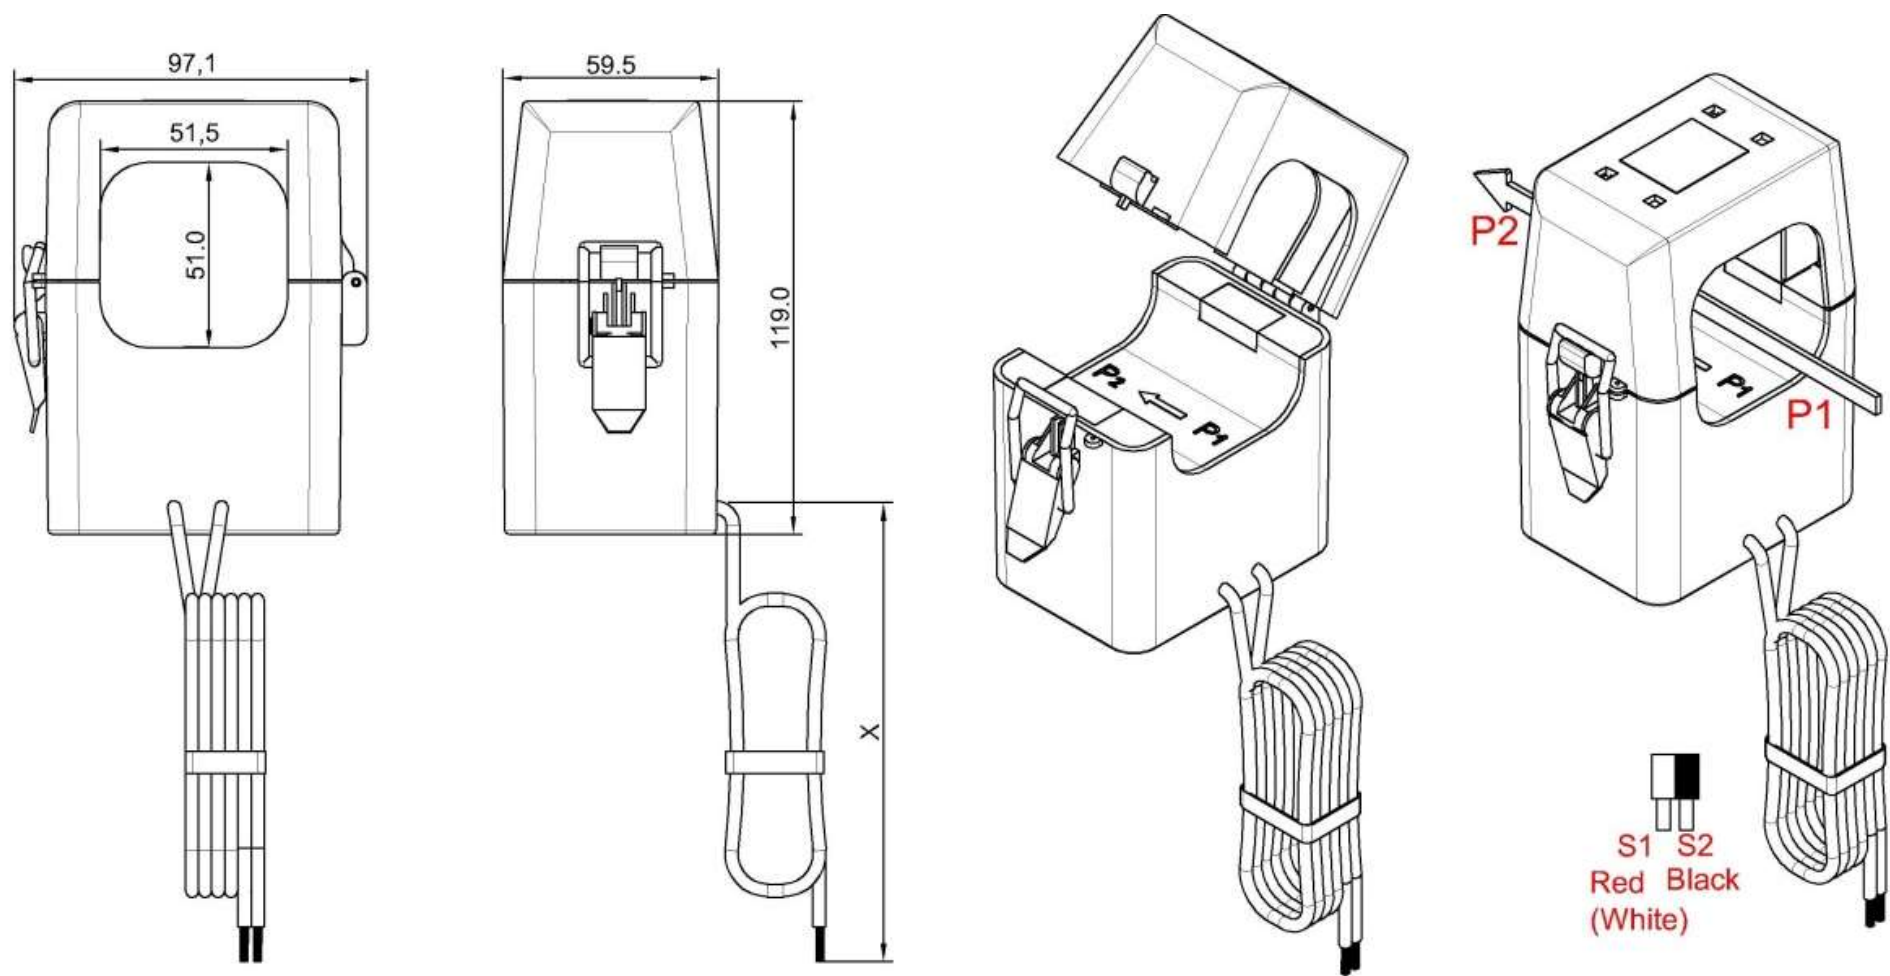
Внешний вид и размеры ТРП-0,66-3/50
